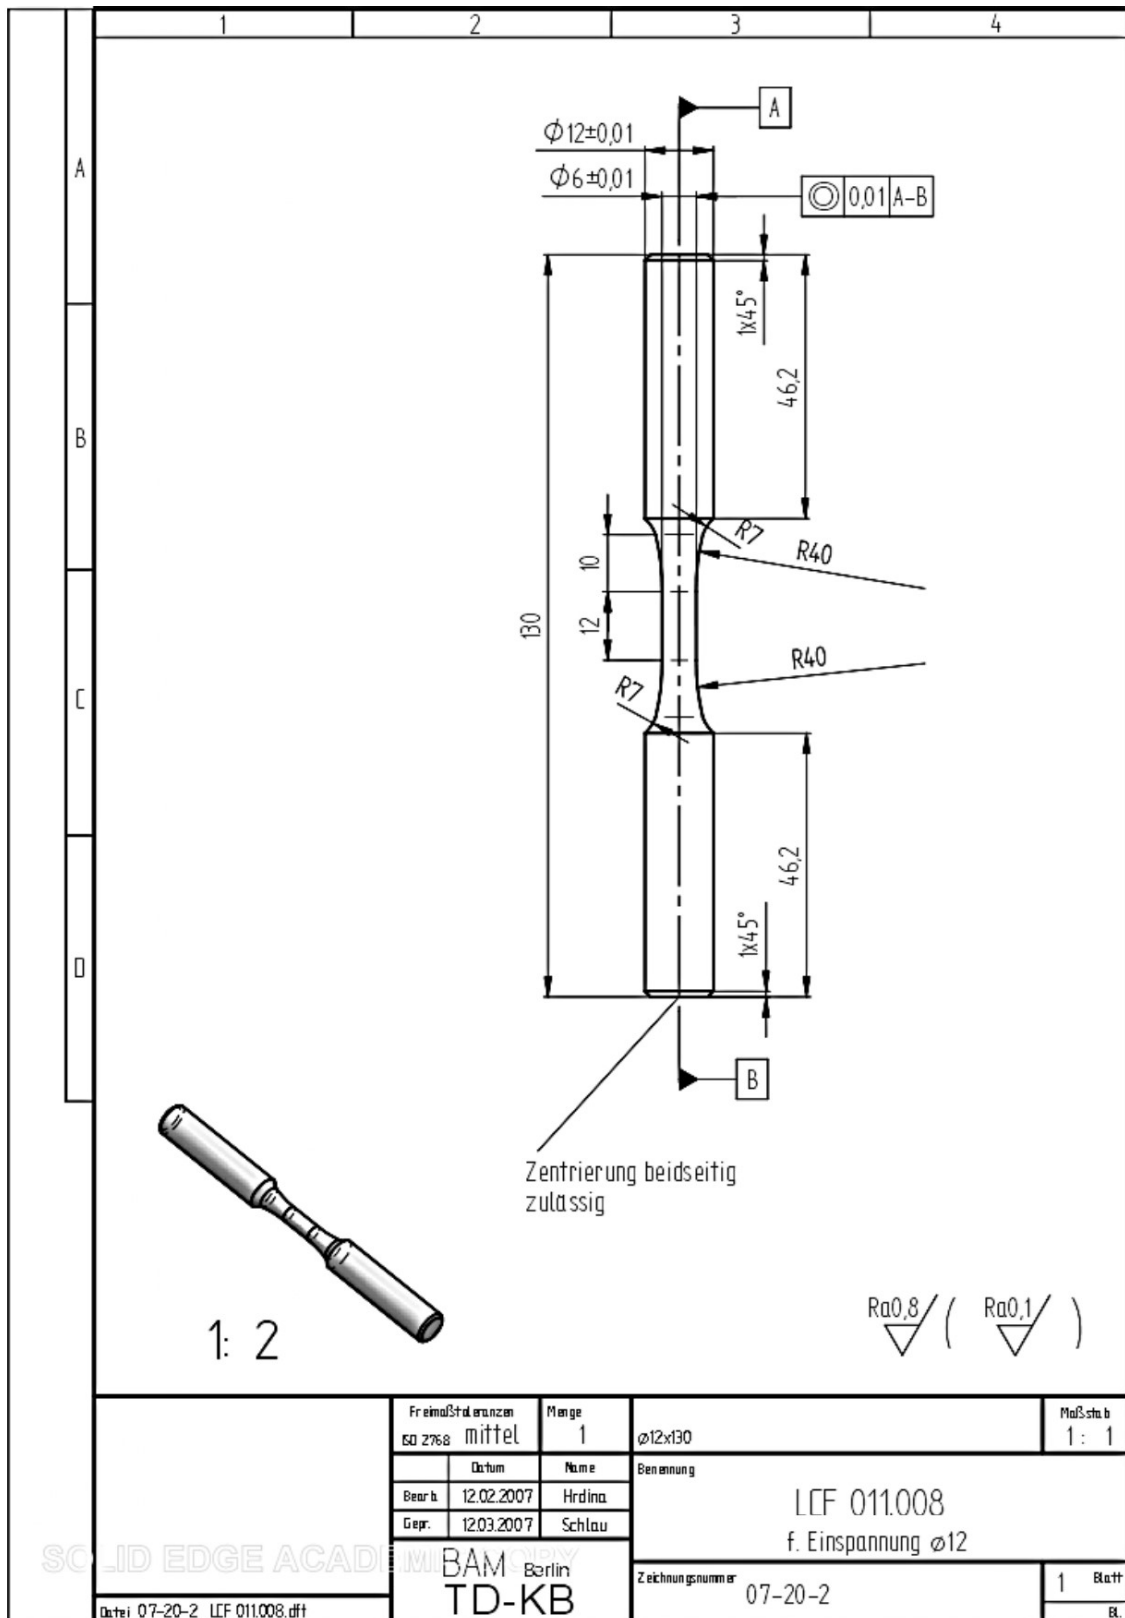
Technische Zeichnung LCF-Proben. Bei den Proben der PBF-LB/M/316L-Werkstoffvariante betrug die Gesamtlänge 110 mm anstatt 130 mm.
